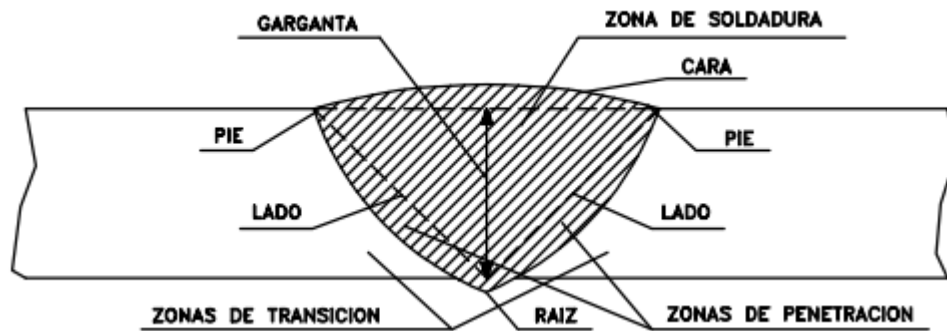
Parts del cordó de soldadura (Font Universidad de Castilla la Mancha)
